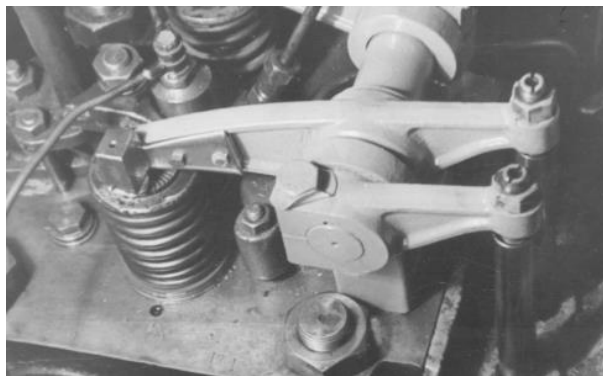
Загальний вигляд храпового механізму обертання клапанів
